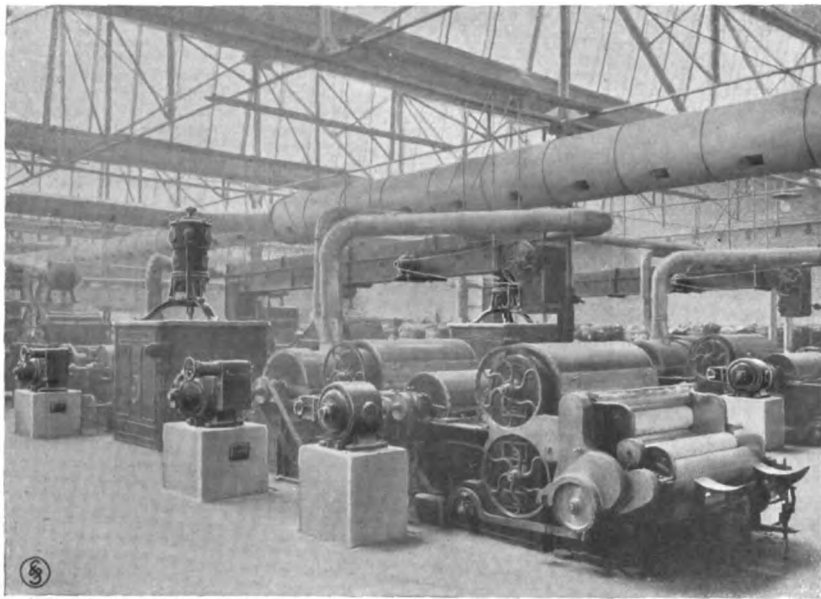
Baumwollöffnersatz: Ballenbrecher, Kastenspeiser, Crightonöffner, Saugöffner, Vorschlagmaschine.
